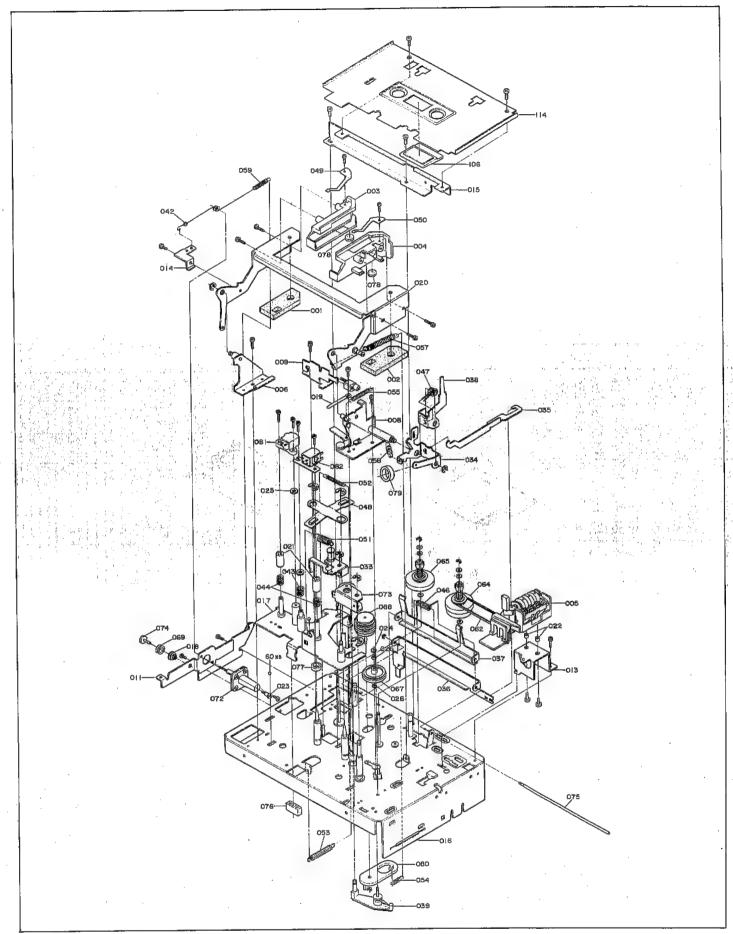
EXPLOSIONSDARSTELLUNG DES MECHANISMUS (ANSICHT VON OBEN)
